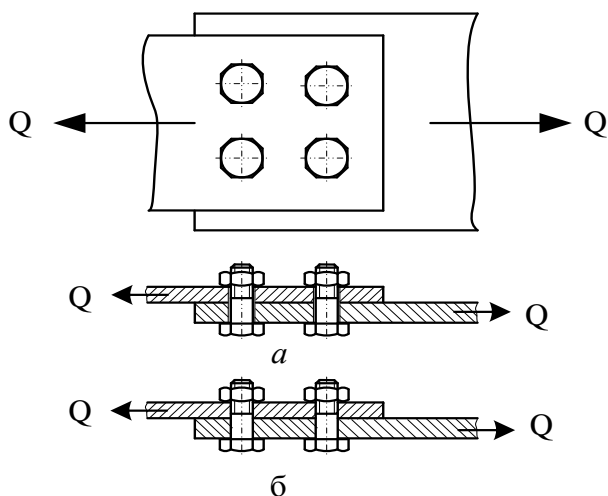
Схема установки болтов в соединении: а – с радиальным зазором; б – под развертку, без радиального зазора
